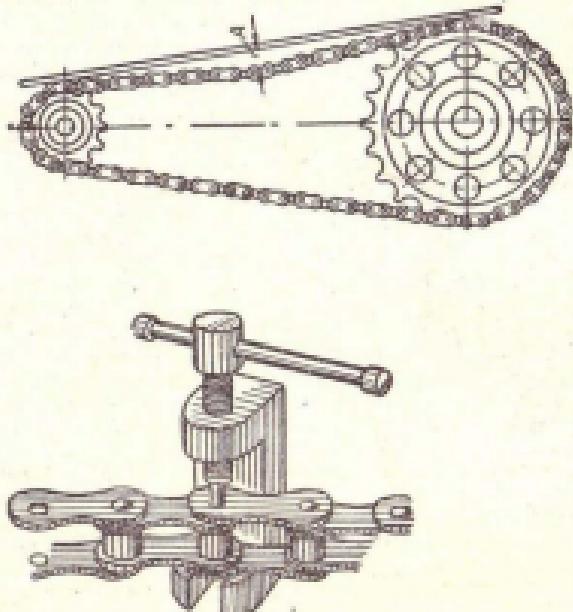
Проверка натяжения и распрессовка звеньев цепи: стрела прогиба  $A=15-20$  мм; винт — струбцина для распрессовки звеньев.
